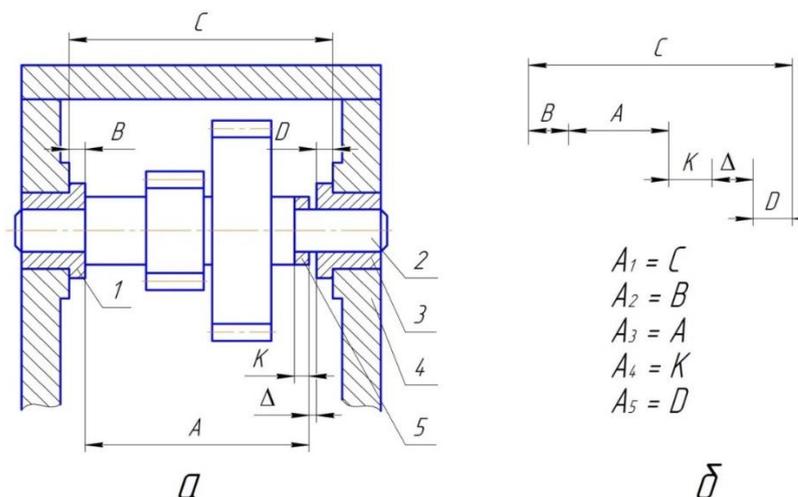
Пример: а — сборочный чертеж, б — схема сборочной размерной цепи
